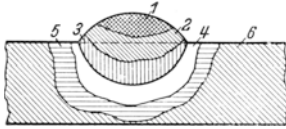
Schema einer Gußeisenkaltschweiße.
